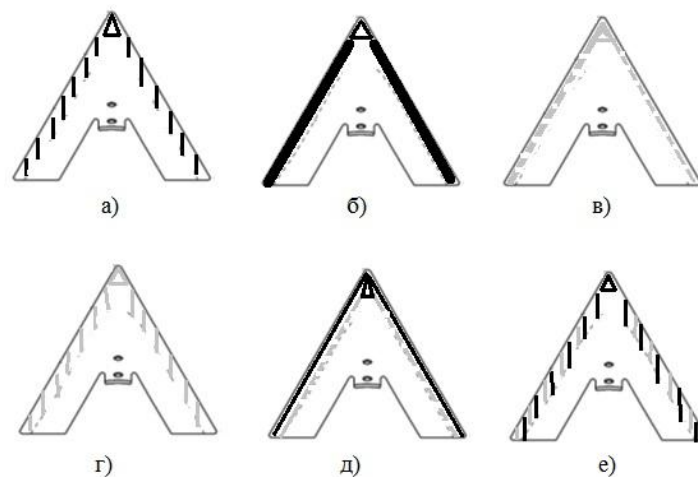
Схема поверхностного упрочнения стрелчатой лапы: а) прерывистая наплавка верхней части лезвия лапы; б) наплавка непрерывным слоем верхней части лезвия; в) наплавка непрерывным слоем нижней части лезвия; г) прерывистая наплавка нижней части лезвия; д) наплавка непрерывным слоем верхней и нижней частей лезвия; е) прерывистая наплавка верхней и нижней частей лезвия
